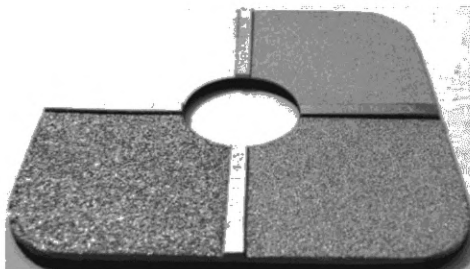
Эталон шероховатости (прибор для оценки шероховатости поверхности)
